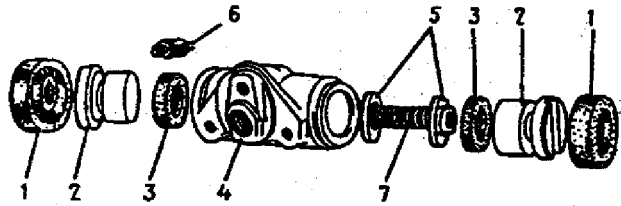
Componentes do cilindro da roda: 1 - coifa; 2 - êmbolo; 3 - gaxeta; 4 - cilindro; 5 - pratos; 6 - sangrador; 7 - mola.
